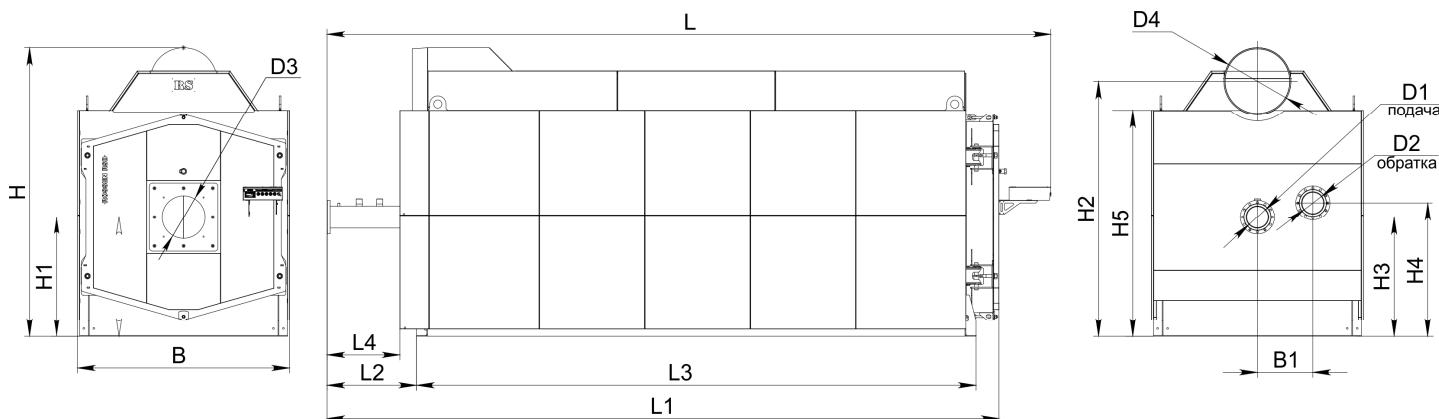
Габаритные и присоединительные размеры котлов RS-D6000 - RS-D10 000
